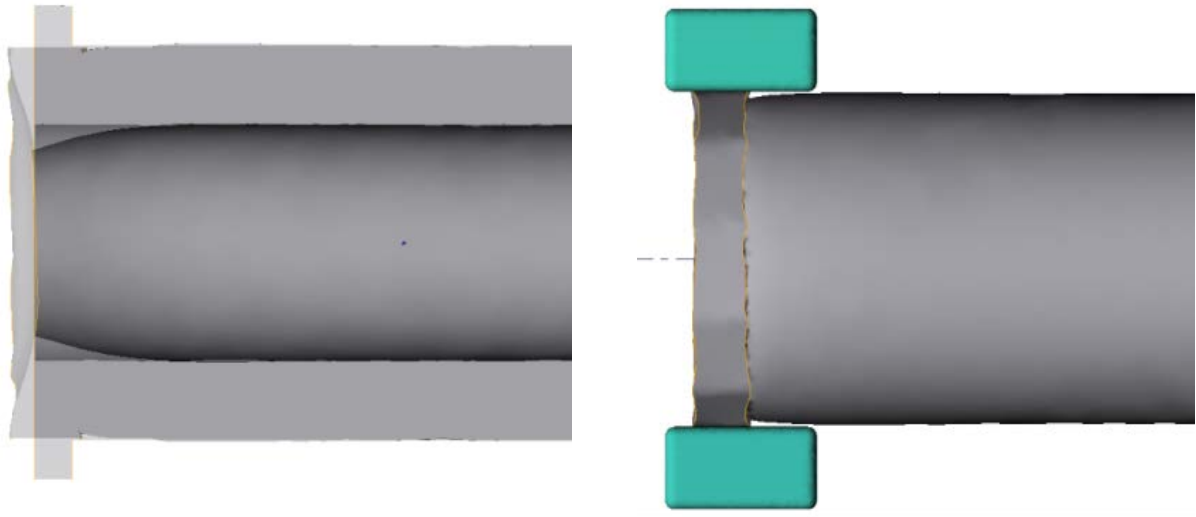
Перерозподіл металу циліндричної заготовки при куванні поковки з внутрішнім отвором
